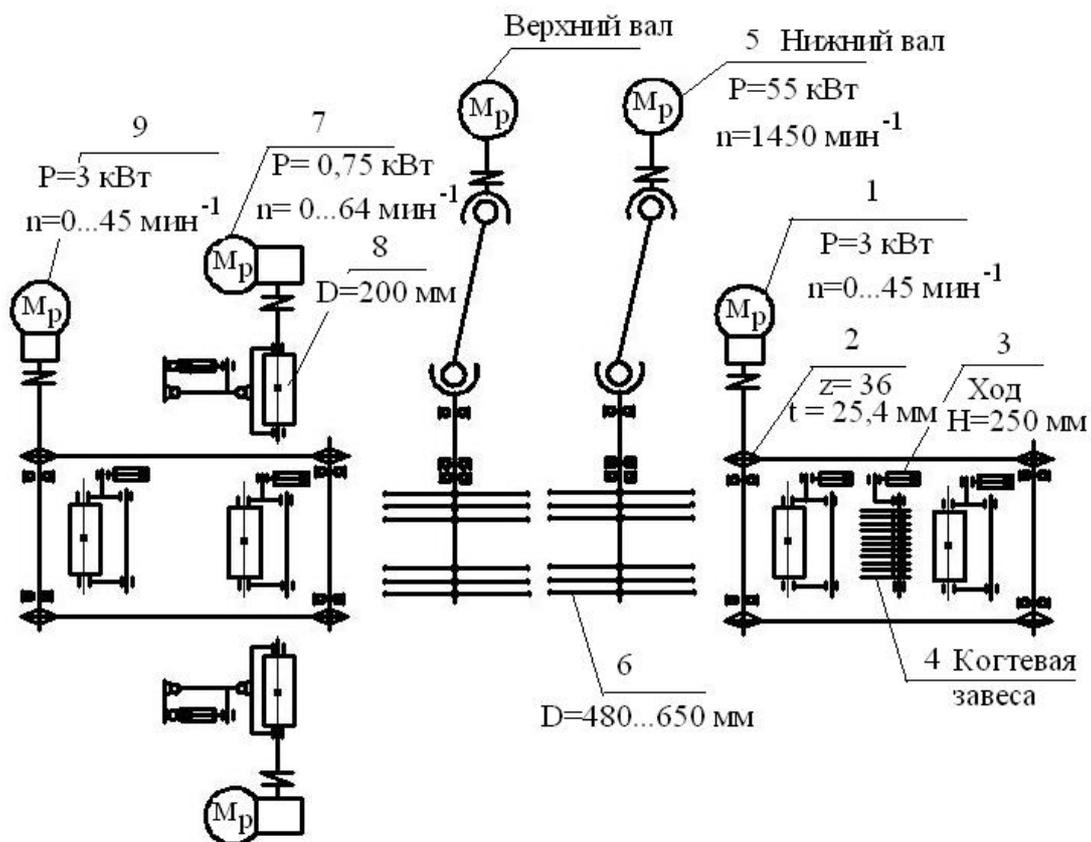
Кинематическая схема бревнопильного станка модели Ц16Б2 «KRAFTER»
